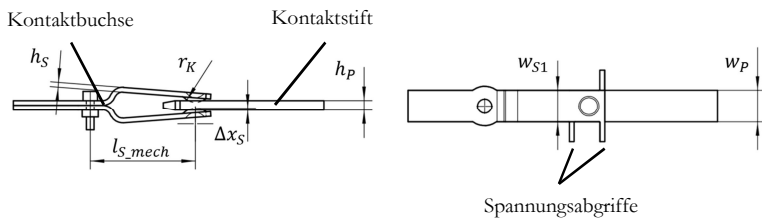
Geometrische Abmessungen des Steckverbinderkontaktes
